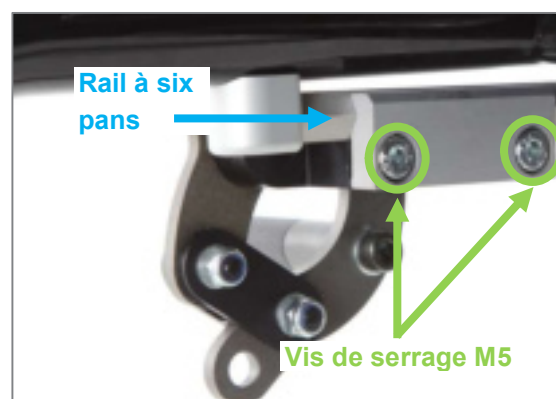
Vis de serrage M5 sur le rail à six pans (vue du côté intérieur du produit)
